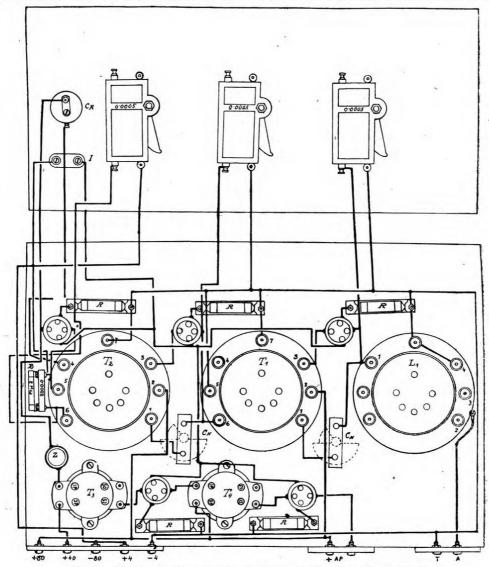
Schema costruttivo: osservare attentamente la disposizione dei collegamenti.
